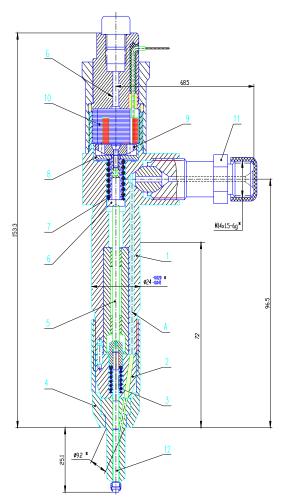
Клапанно-щелевая форсунка с электронным управлением: 1-корпус форсунки; 2-проставка; 3-пружина форсунки; 4-гайка распылителя; 5-штанга; 6-упор; 7-пружина; 8-экран; 9-якорь; 10-электромагнит; 11-штуцер подвода топлива; 12-клапан форсунки.
